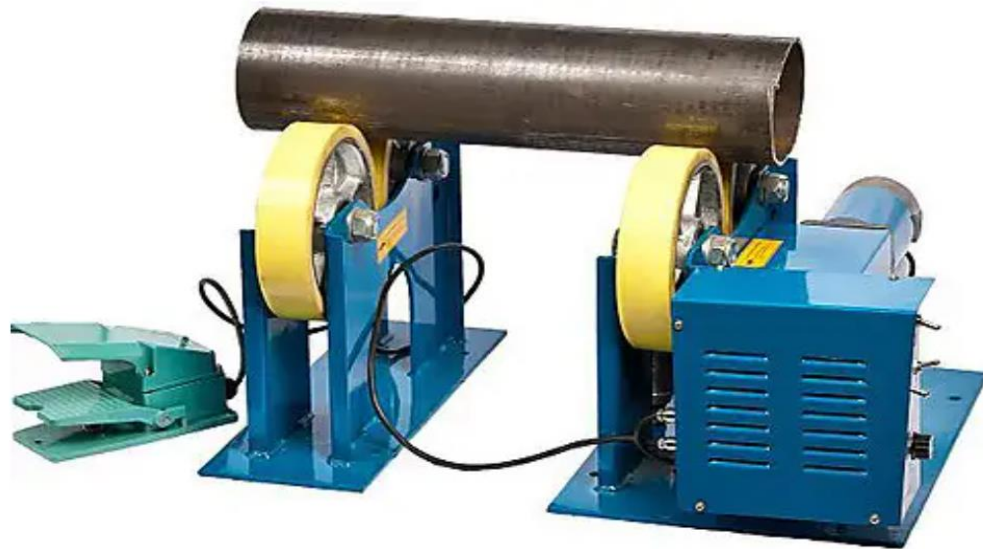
Універсальний зварювальний обертач- NNTR-1000
